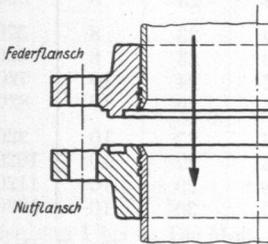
Flansch mit Nut und Feder, DIN 2512.
